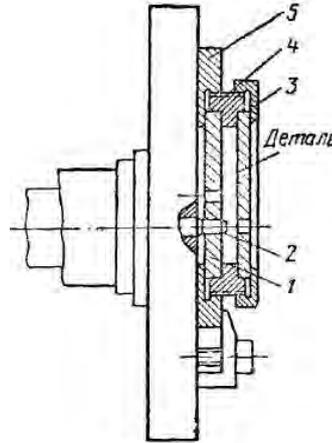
Схема приспособления для сверления по установочным шаблонам
